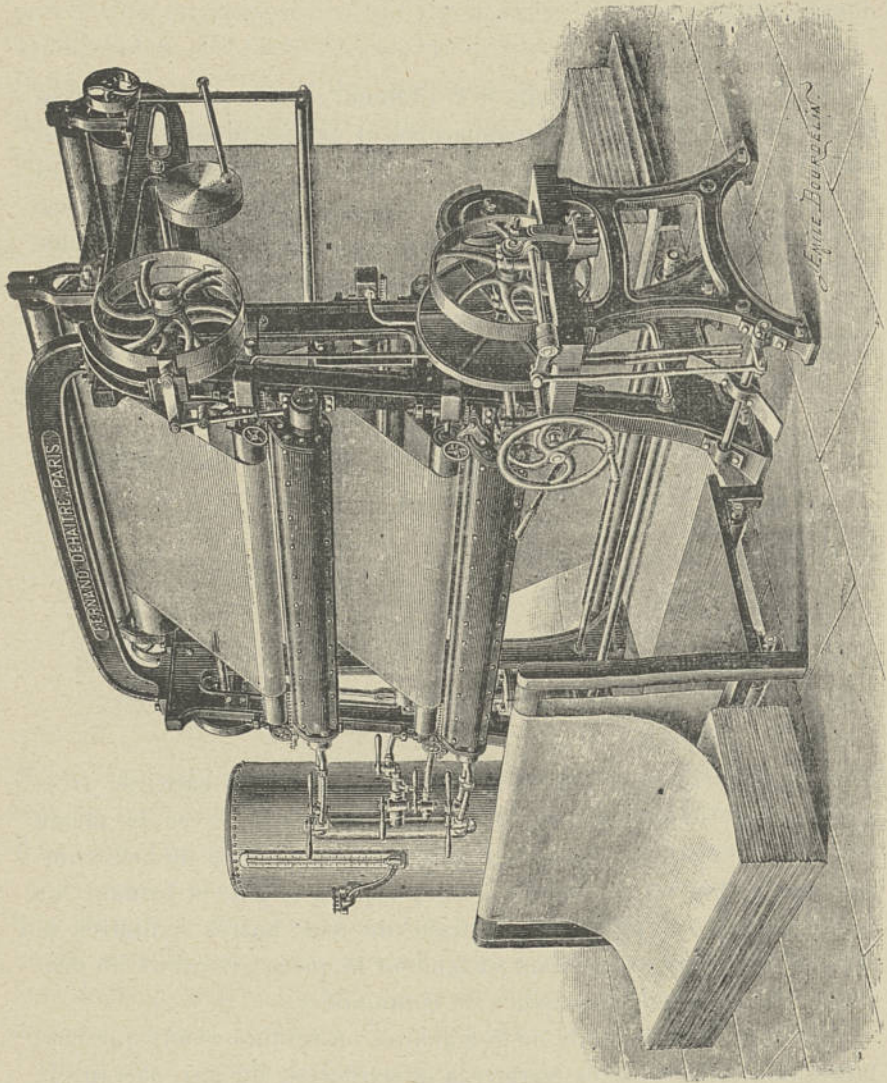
Machine à griller à rampe Descat-Leleux.
